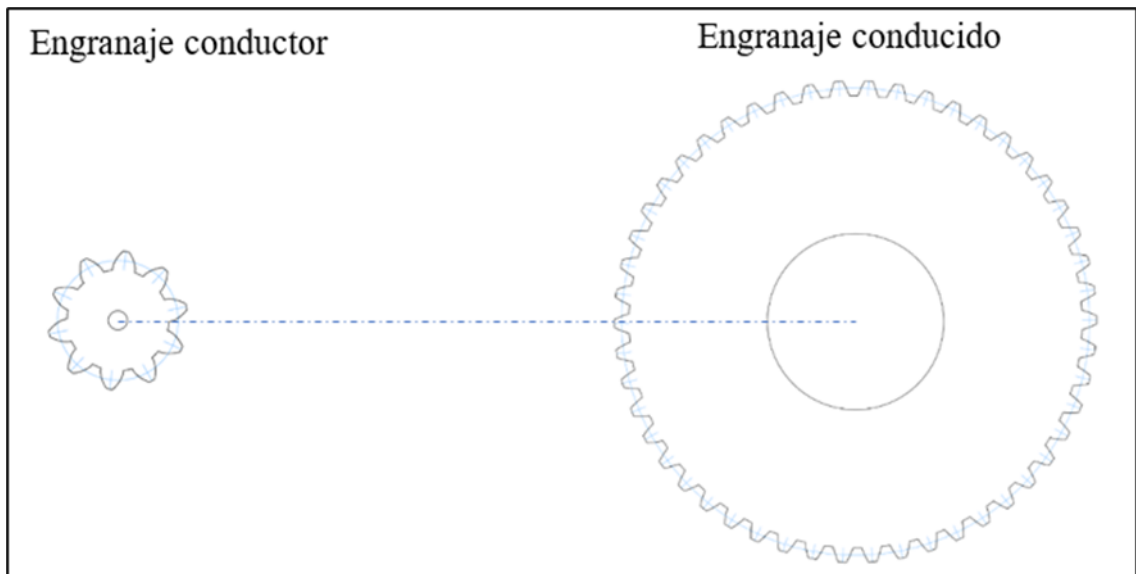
Boceto de los engranajes del sistema de transmisión
